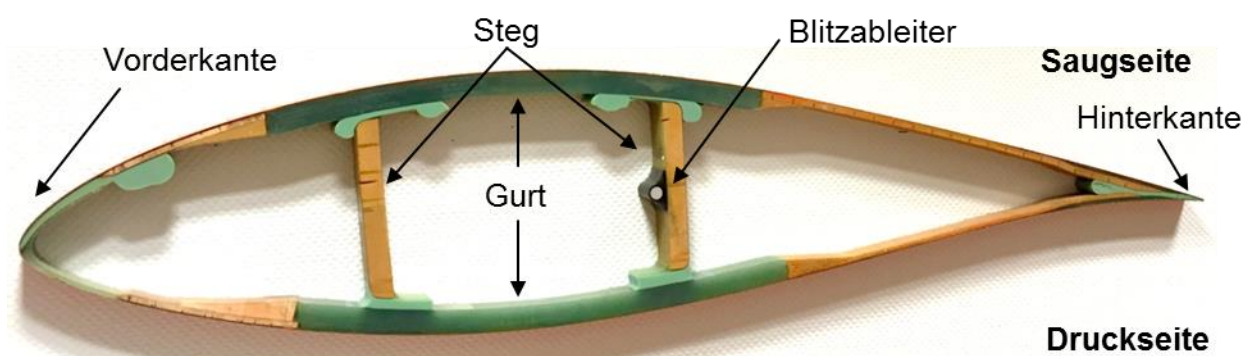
Querschnitt eines Rotorblatts in aktueller Bauweise.
